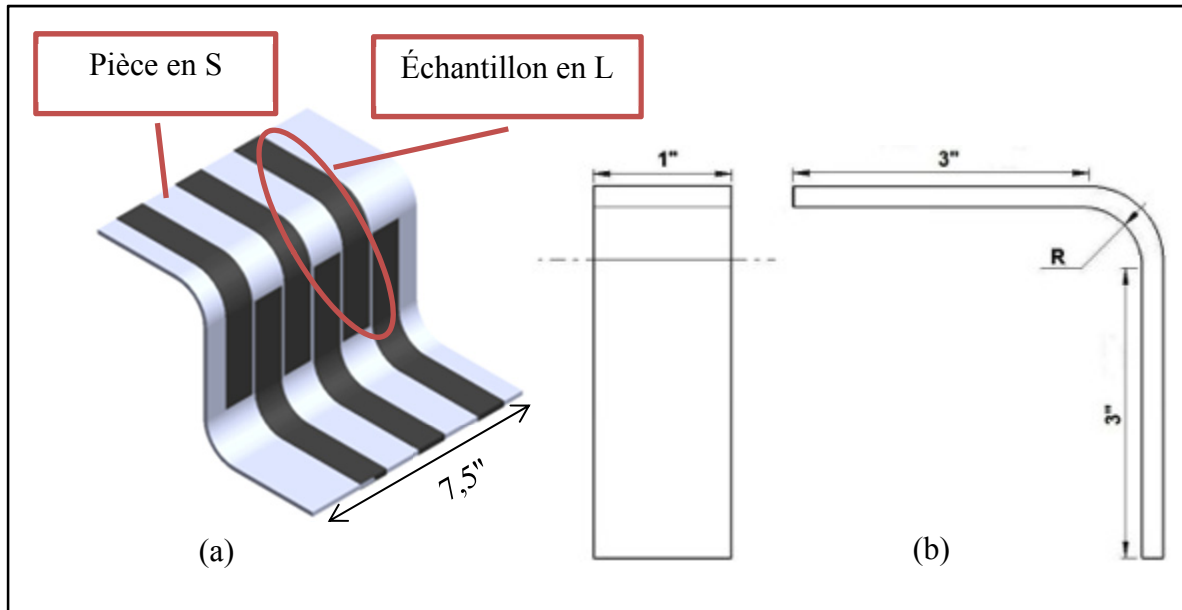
Emplacement (a) et dimensions (b) des échantillons extraits des pièces estampées avec le moule M3
